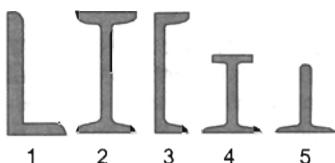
Некоторые металлические профили: 1 — угловой; 2 — двутавровый; 3 — швеллерный; 4 — железнодорожный рельс; 5 — тавровый
